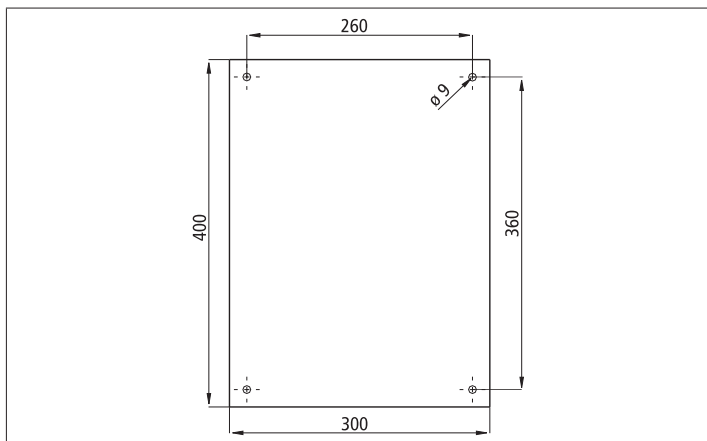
Rückansicht SVG 522/TSK 03 ohne Befestigungslaschen
